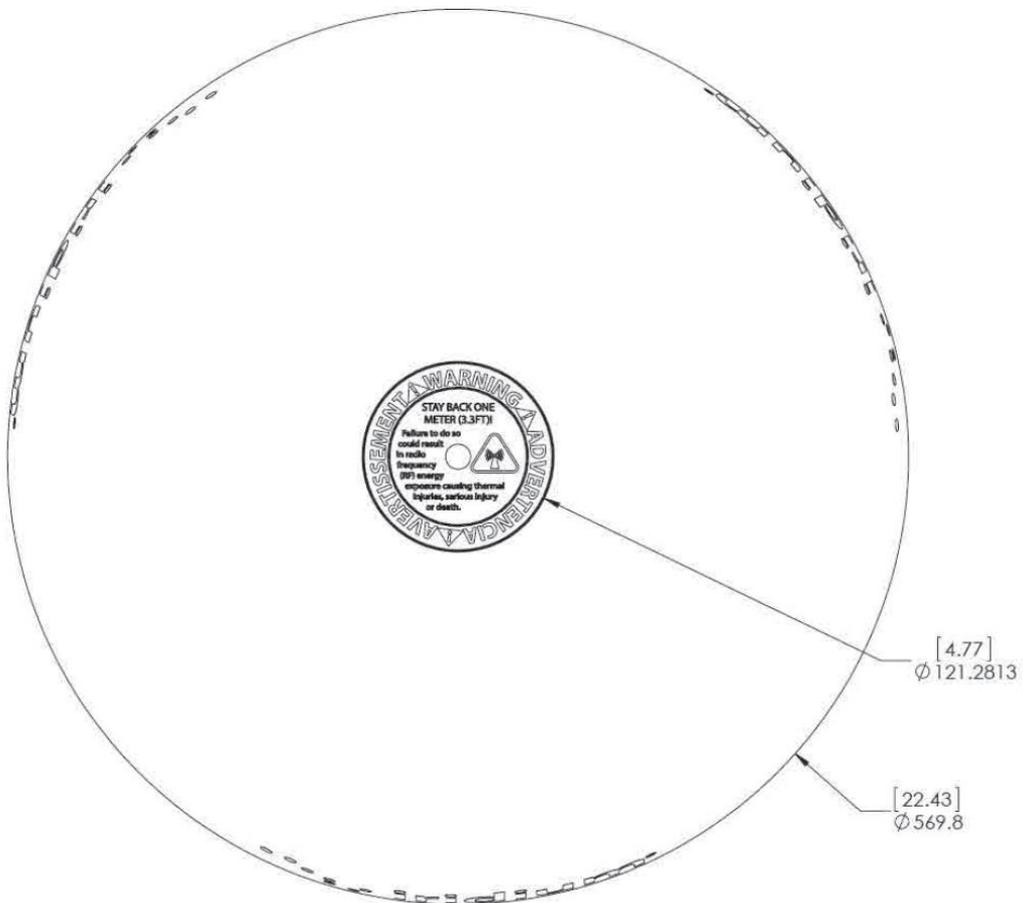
Надпалубное оборудование (ADE) - Вид сбоку и сверху
